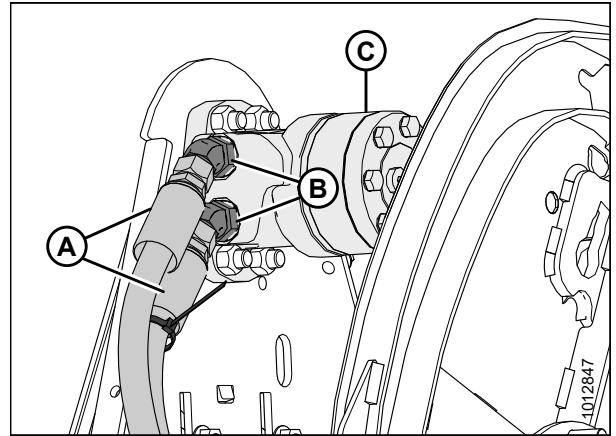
Haspelmotor und Hydraulikschläuche
